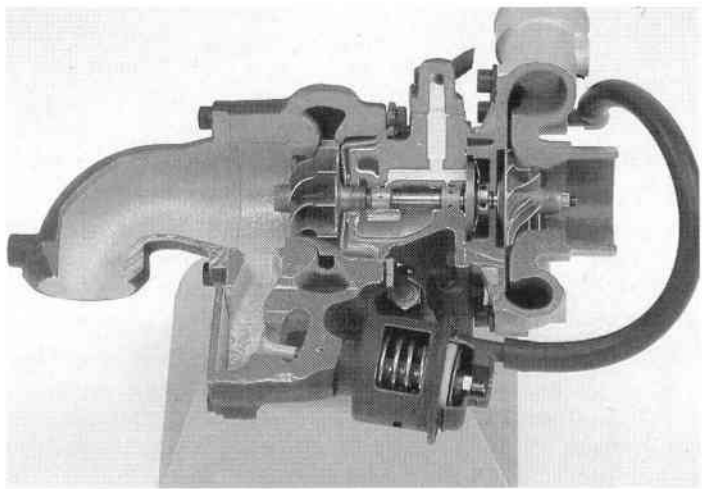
Vue d'un turbo-compresseur avec soupape by-pass de régulation (Coupe et photo CEMAGREF-DICOVA).
